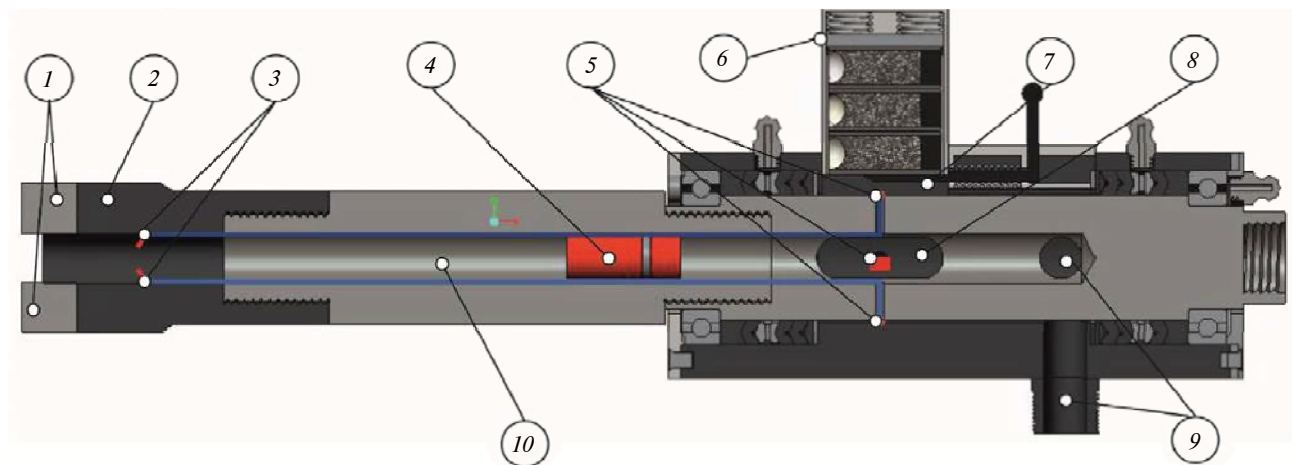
Конструкція механізму для вибухо-механічного руйнування гірських порід: 1 – різці; 2 – різальний інструмент; 3 – пластини контактні; 4 – заряд вибухової речовини; 5 – напайки контактні; 6 – касета із зарядами вибухової речовини; 7 – затвор; 8 – отвір для подачі зарядів вибухової речовини до продувного каналу; 9 – отвори для нагнітання стисненого повітря; 10 – продувний канал
